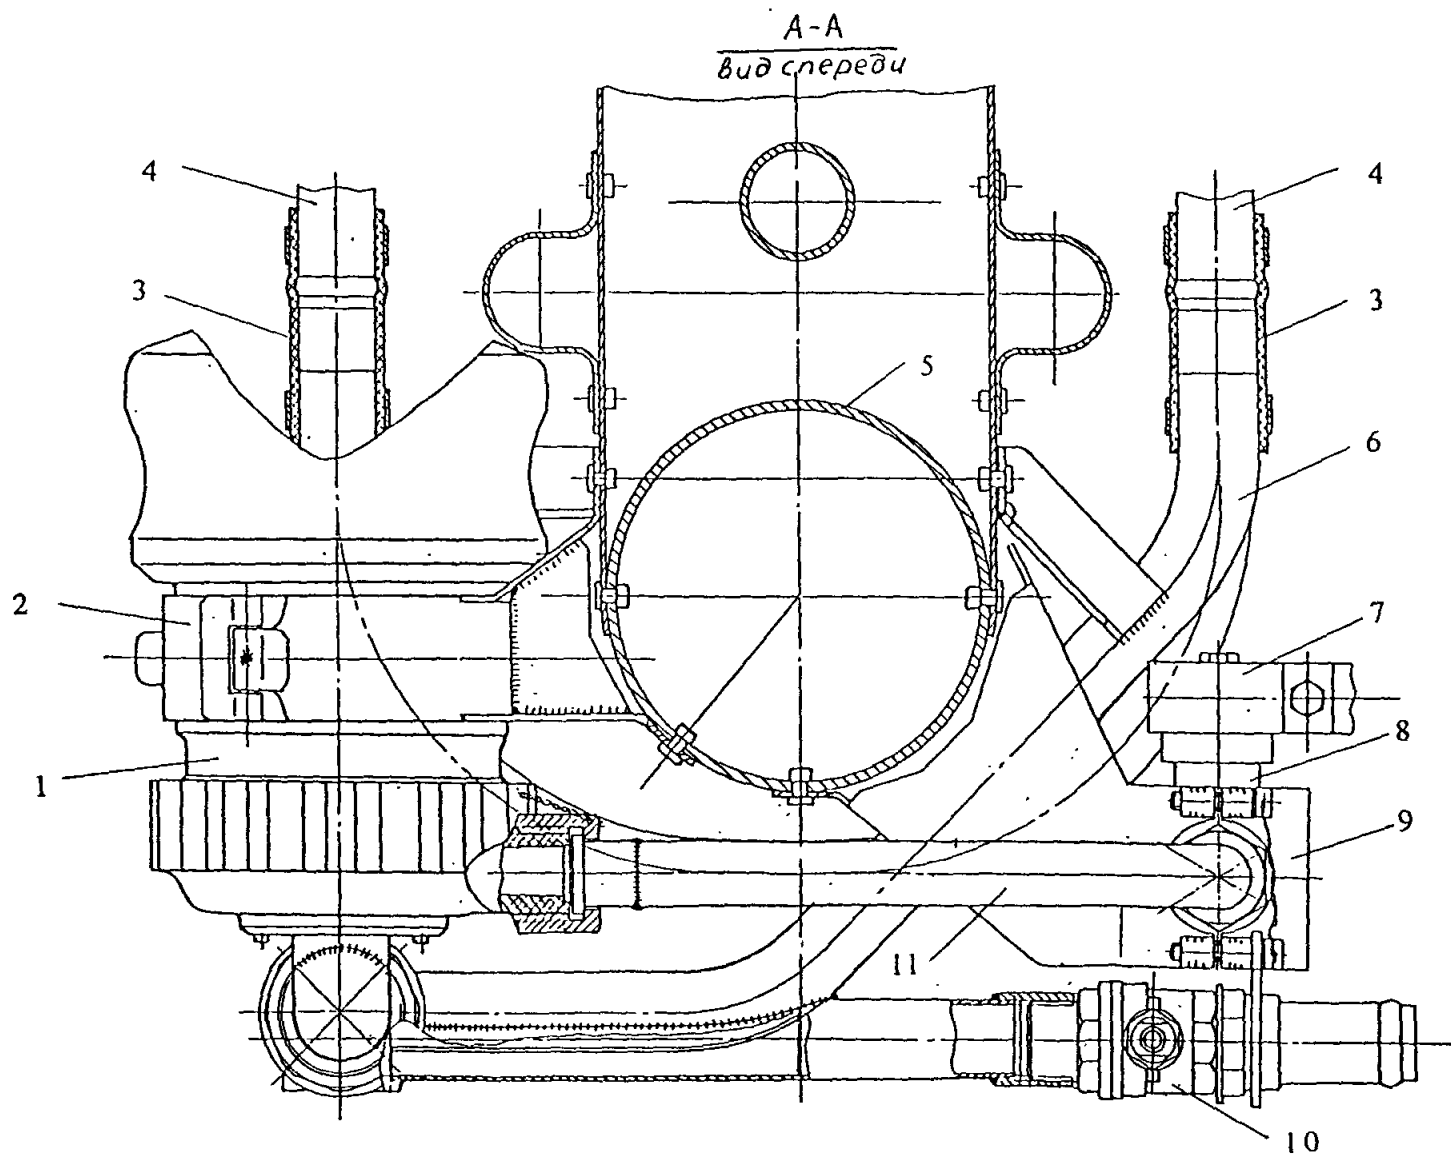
Монтажная схема сельскохозяйственного оборудования
